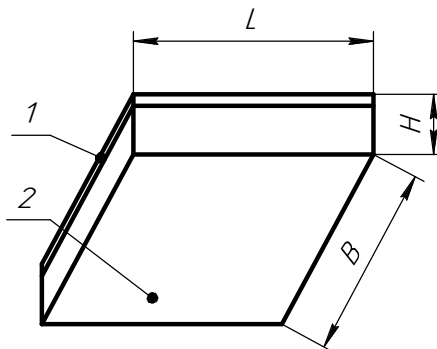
ЛПО46-4x14; 1. Корпус в сборе, 2. Рассеиватель
